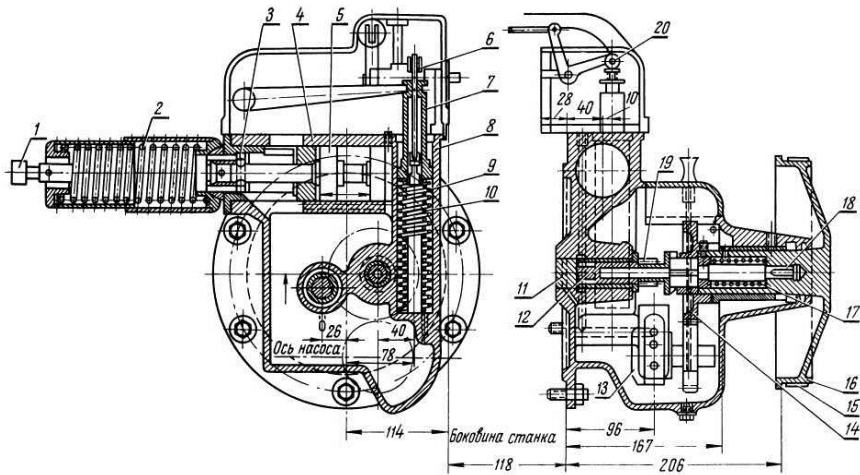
Автомат гідрокерування станка ЗМ: 1 – гвинт; 2, 9, 10, 17 – пружина; 3 – шарнір шарової опори; 4, 11 – циліндр гідравлічний; 5, 7, 12 – поршень; 6 – золотник; 8 – циліндр дросельний; 13 – насос масляний; 14 – колесо зубчасте; 15 – пасок приводний; 16 – шків; 18 – вал; 19 – напівмуфта; 20 – важіль
